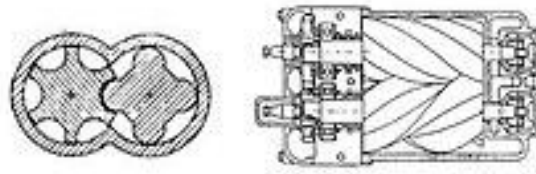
Схематическое изображение винтового блока воздушного компрессора
